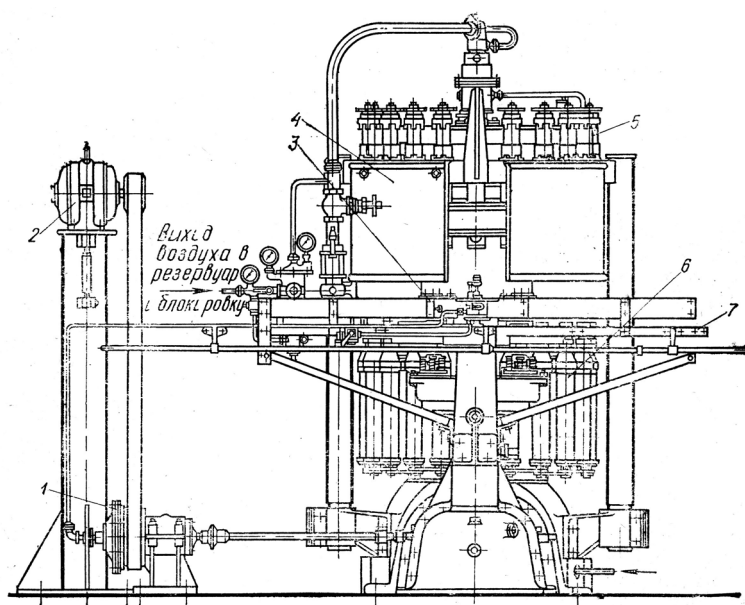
Розливочна машина марки РГМ-3:
